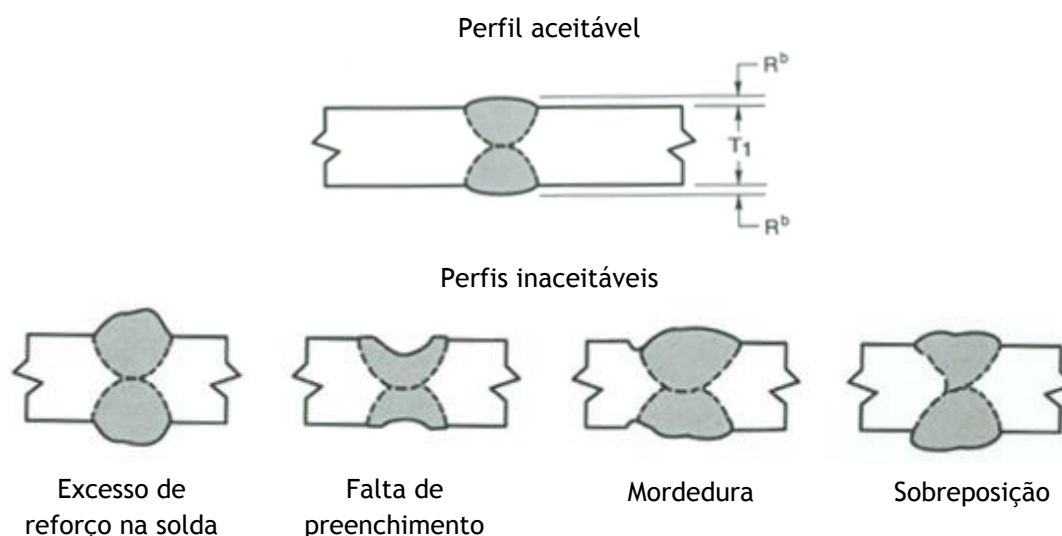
Perfis de cordões de soldadura aceitáveis e inaceitáveis
